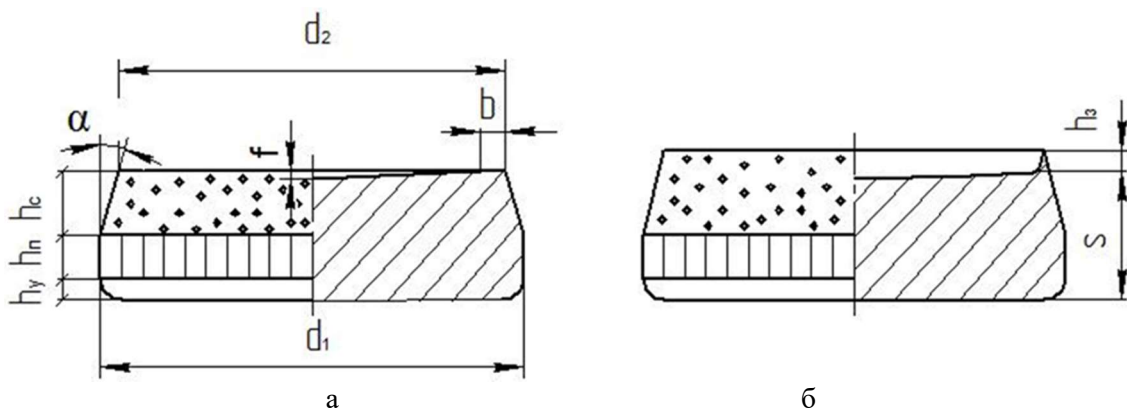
Профиль поверхности среза вырубленной детали с острыми (а) и притупленными (б) кромками пуансона
